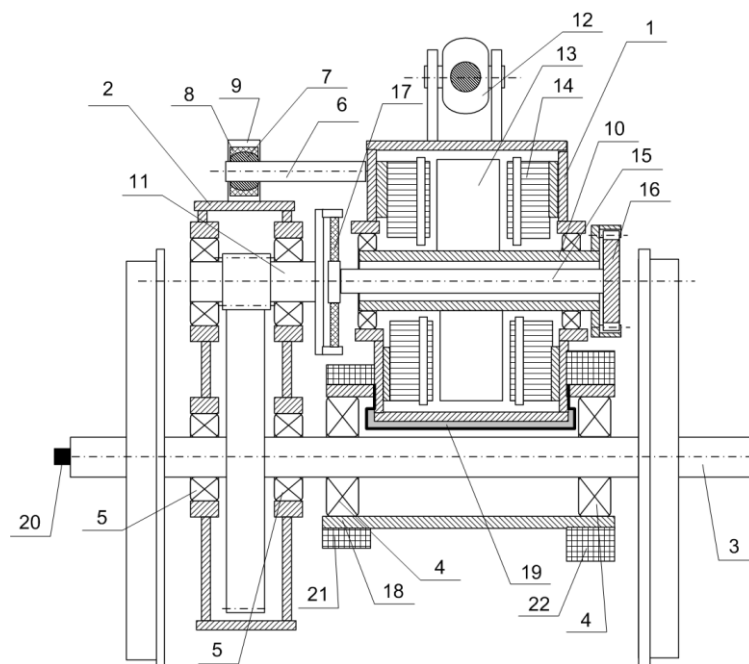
Общая схема агрегатного тягового привода с асинхронным тяговым электродвигателем с дисковым ротором: 1 – тяговый двигатель; 2 – осевой редуктор; 3 – ось колесной пары; 4, 5 – осевые подшипники; 6 – палец; 7 – сферический шарнир; 8 – ползун; 9 – кронштейн; 10 – вал ТЭД; 11 – вал осевого редуктора; 12 – подвеска; 13 – ротор; 14 – статор; 15 – торсионный вал; 16 – зубчатая муфта; 17 – резинокордная муфта; 18 – труба; 19 – вырез; 20 – токосъемное устройство; 21, 22 – индукторы
